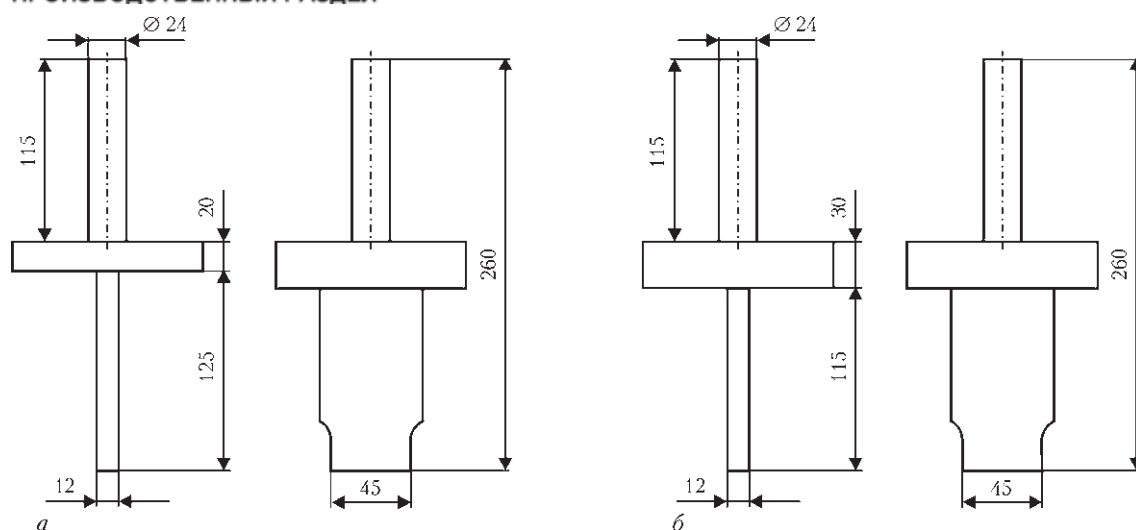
Чертеж модельного образца сварного соединения шпильки крепления плит БМП с верхним поясом тавровой балки из сталей Ст3сп (а) и 09Г2С (б) соответственно вторая и третья серии образцов
